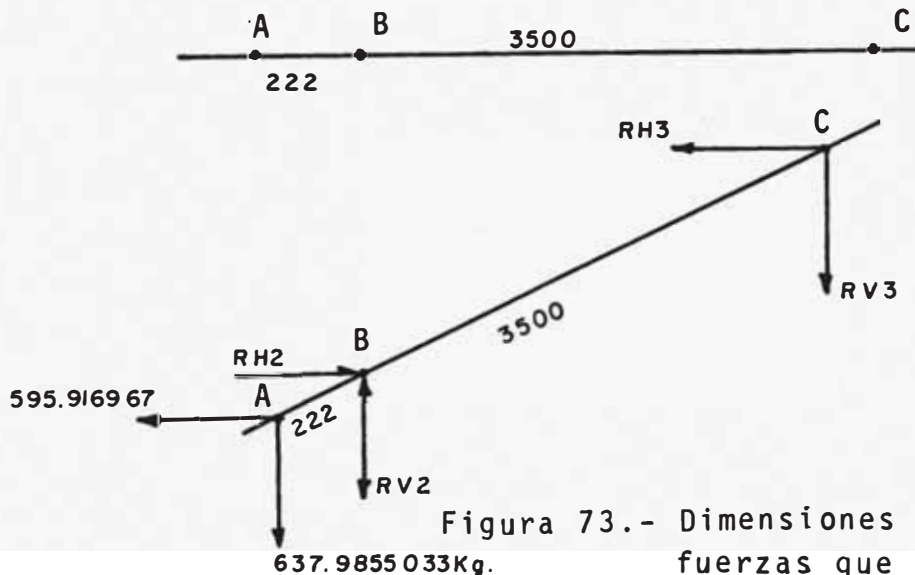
Dimensiones del Eje y fuerzas que actúan
